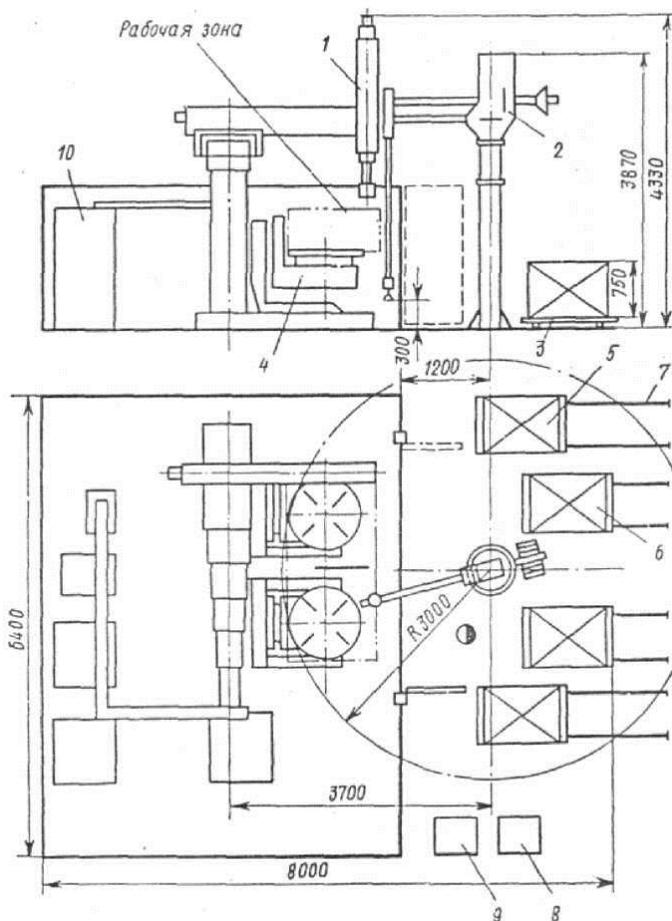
Пример планировки робототехнического комплекса дуговой сварки
